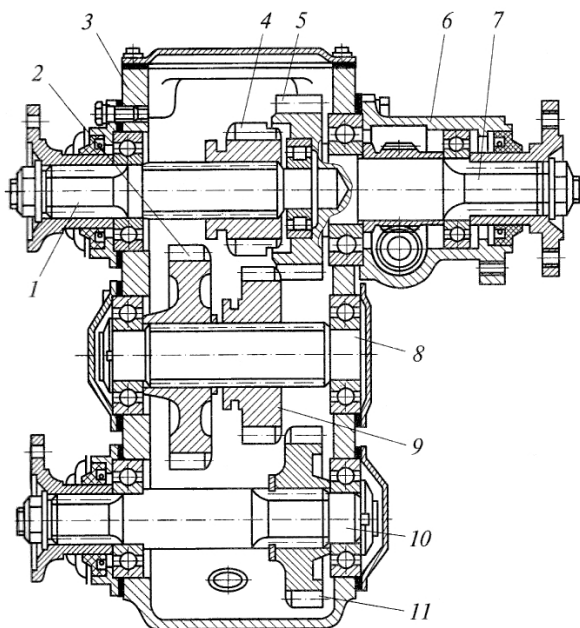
Раздаточная коробка автомобиля ГАЗ
